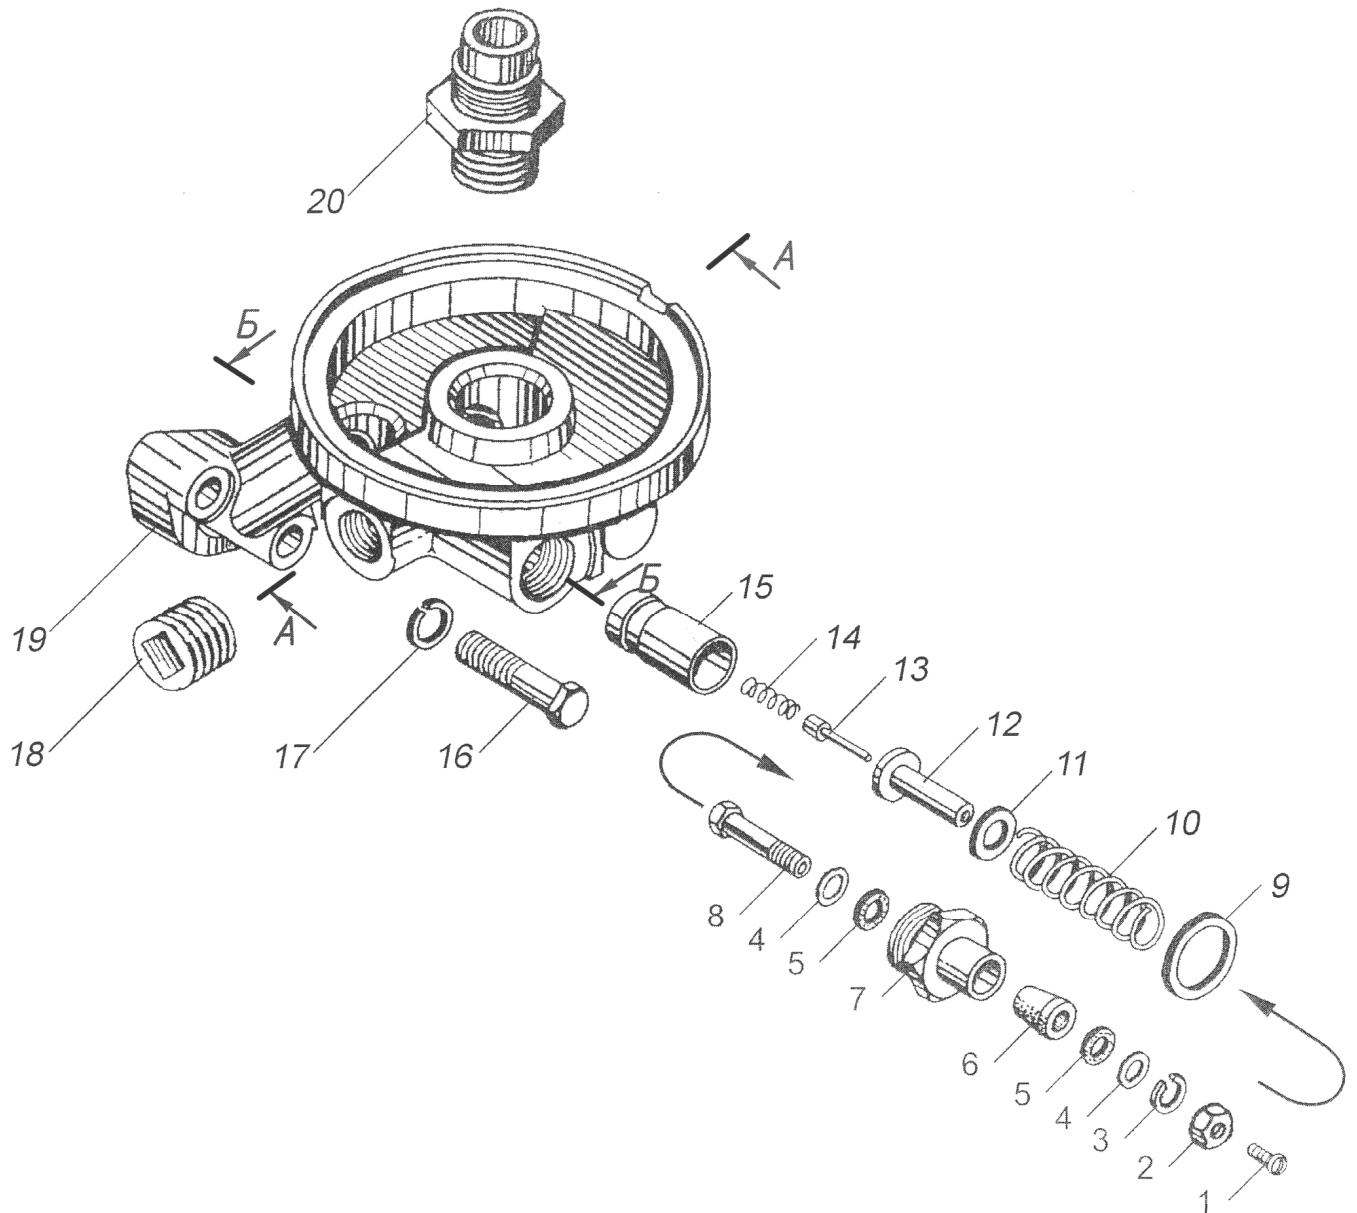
Корпус масляного фильтра в сборе (изометрия)
